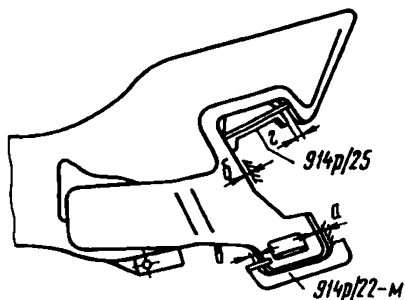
Зазоры для определения толщины слоя наплавки поверхностей по контуру зацепления корпуса автосцепки
